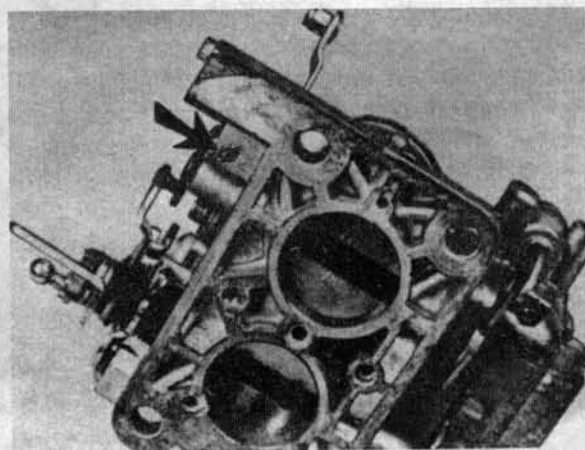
Карбюратор Weber 32 DIR – регулировочный опорный винт заслонки (обозначен стрелкой)
